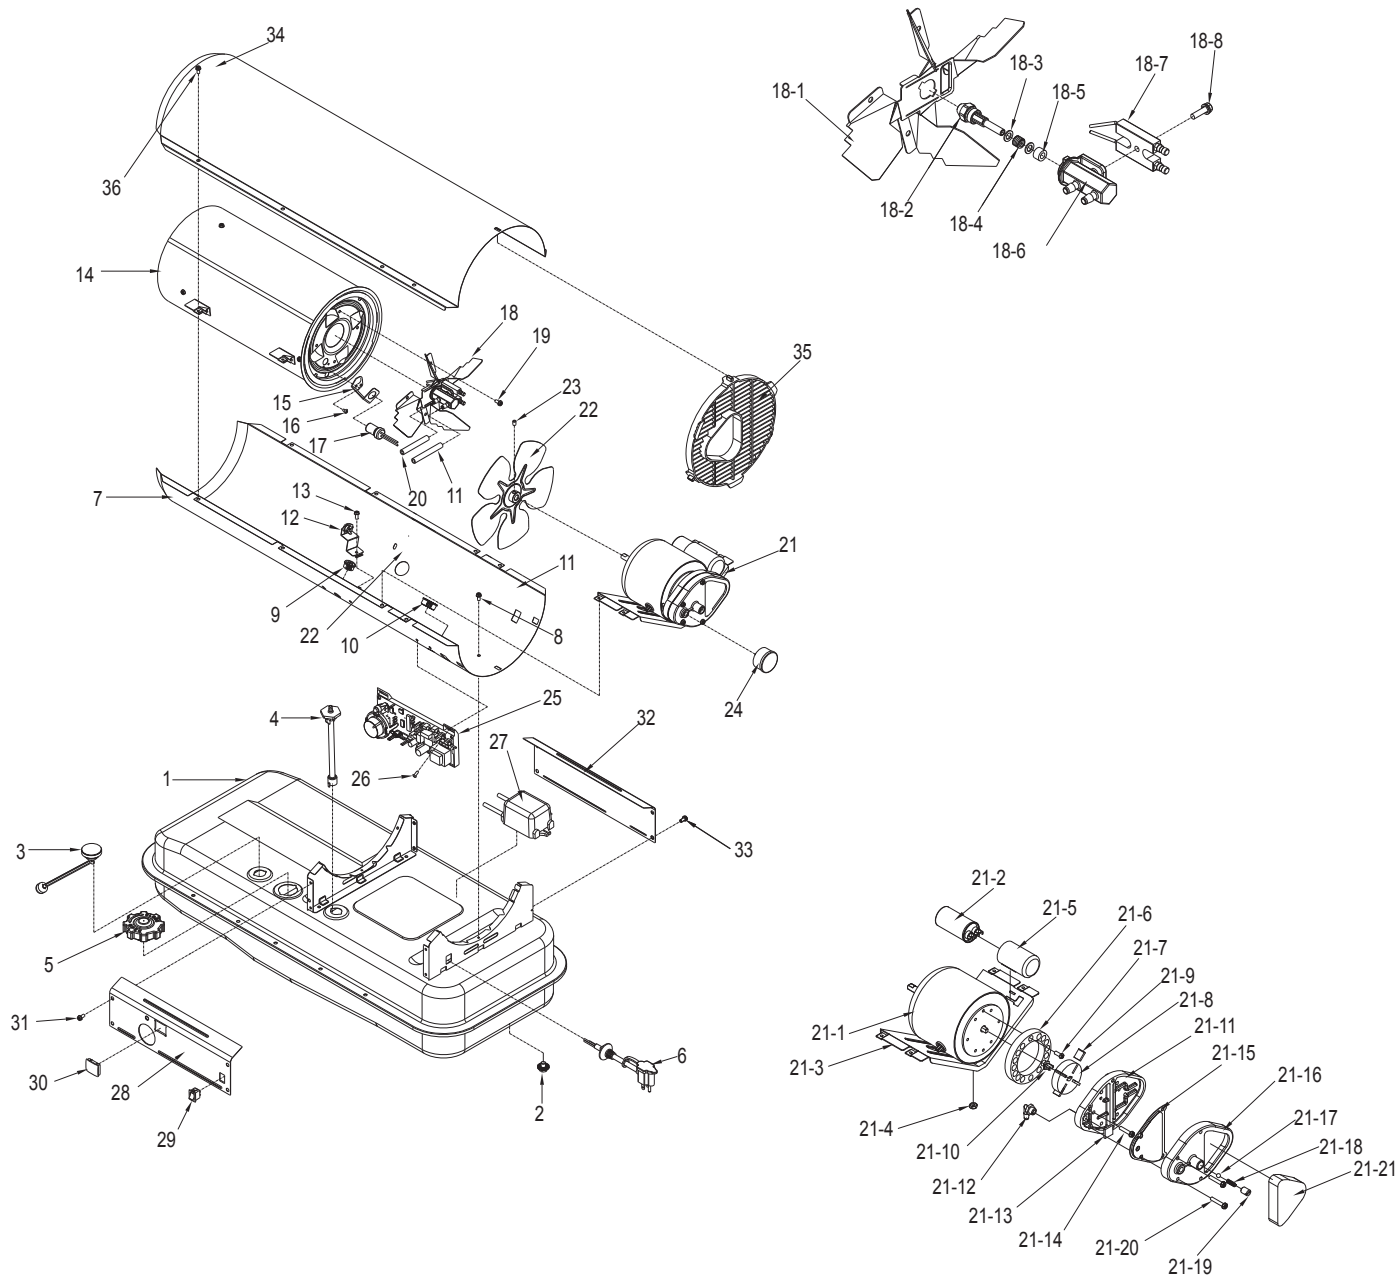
Illustration des pièces détachées pour radiateur portable à l'huile modèle 3VE521
